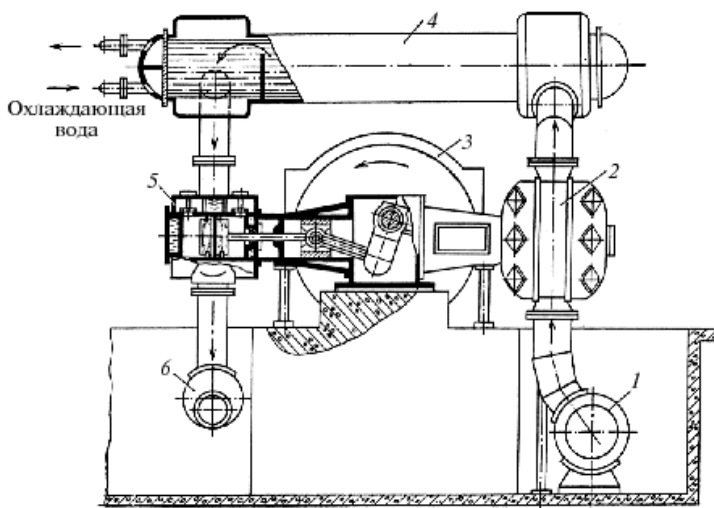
Двухступенчатый оппозитный компрессор типа ВМ
